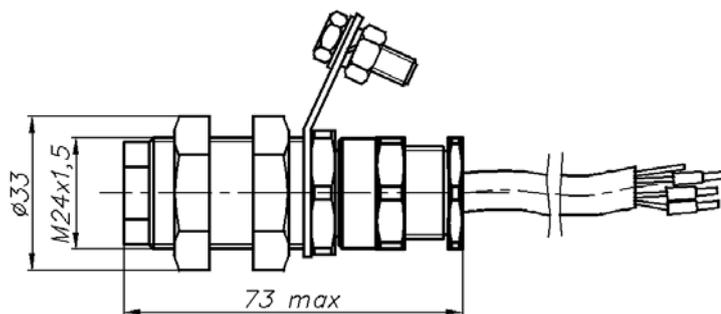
Внешний вид и габаритные размеры датчика ДКПГ исполнение 8
